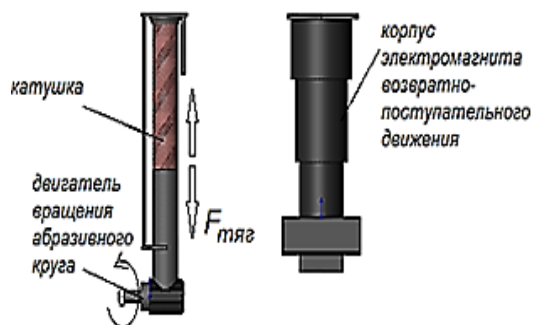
Силовая головка с электромагнитным приводом подачи, обеспечивающая постоянную силу прижима круга к обрабатываемой поверхности лопатки
